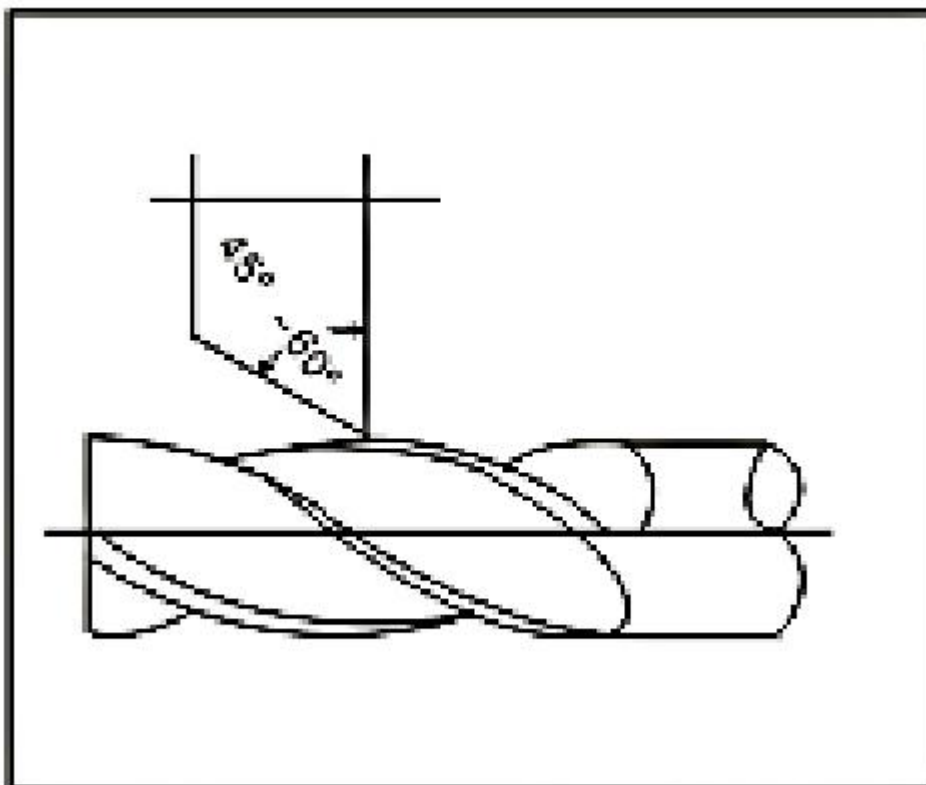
Форма шлифовального круга, используемая для заточки вогнутой дугообразной формы задней поверхности кромки.
